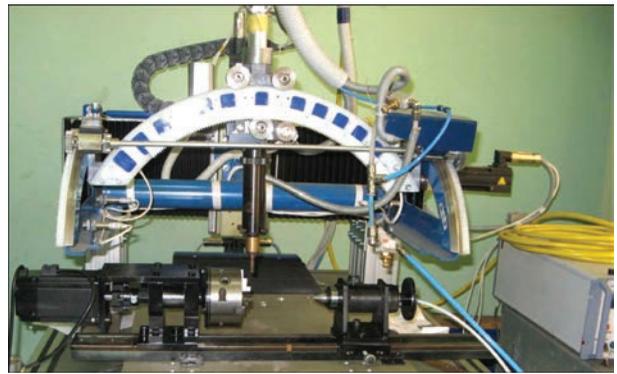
Технологический комплекс для лазерной сварки сильфонных компенсаторов
